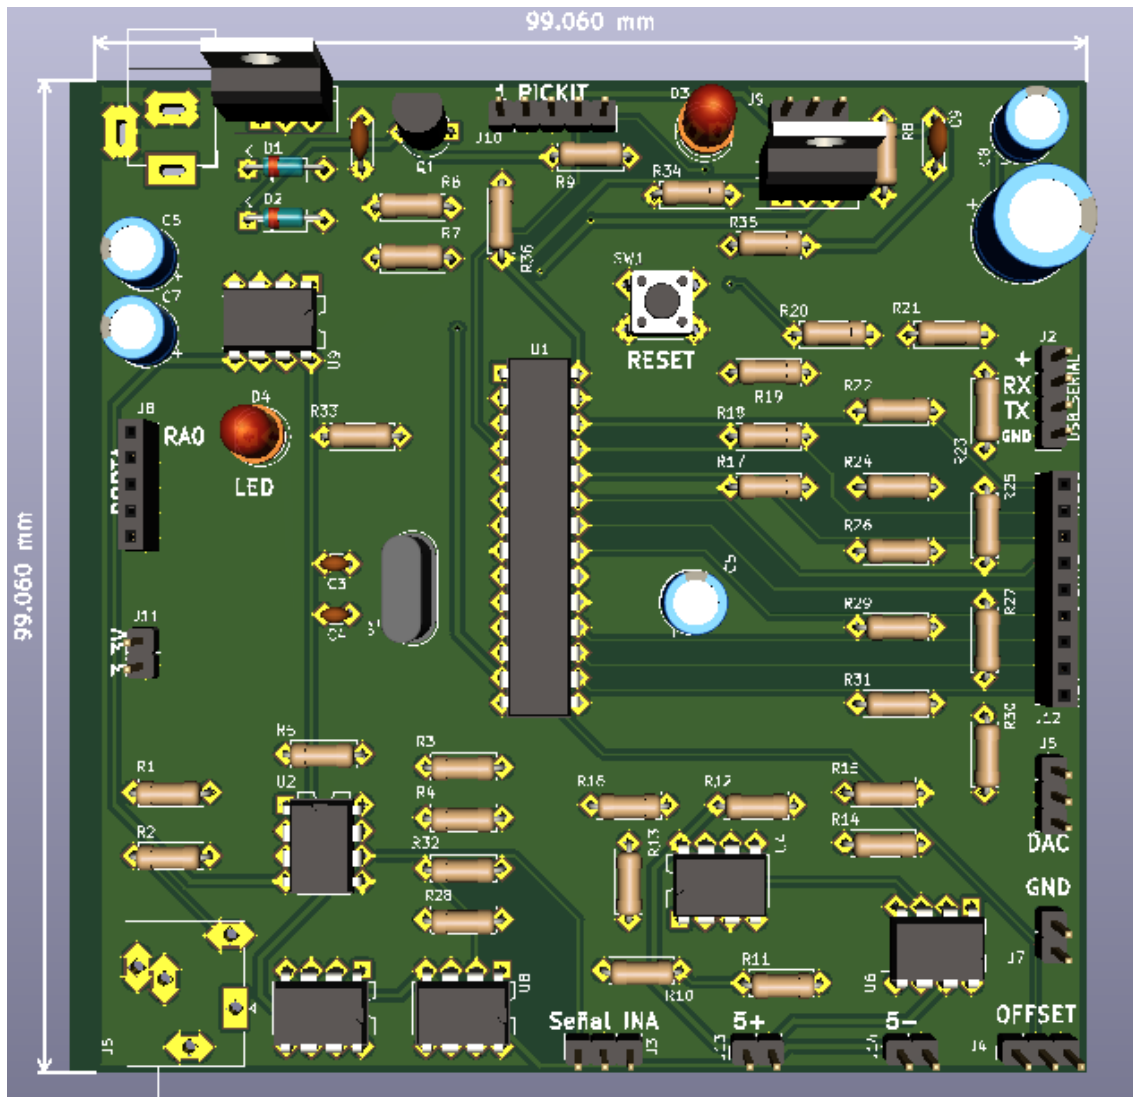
PCB de la investigación. Desarrollada en KiCad 5.0. Elaboración propia
